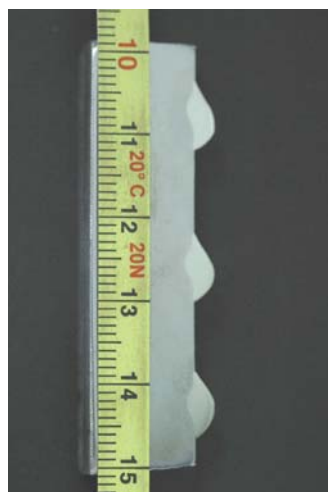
Seção transversal dos cordões de solda da figura 3.6.
